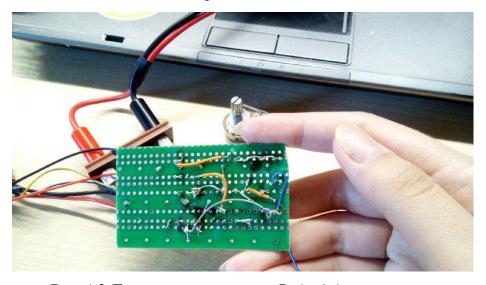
Готовий прототип. Вид з'єднання елементів
